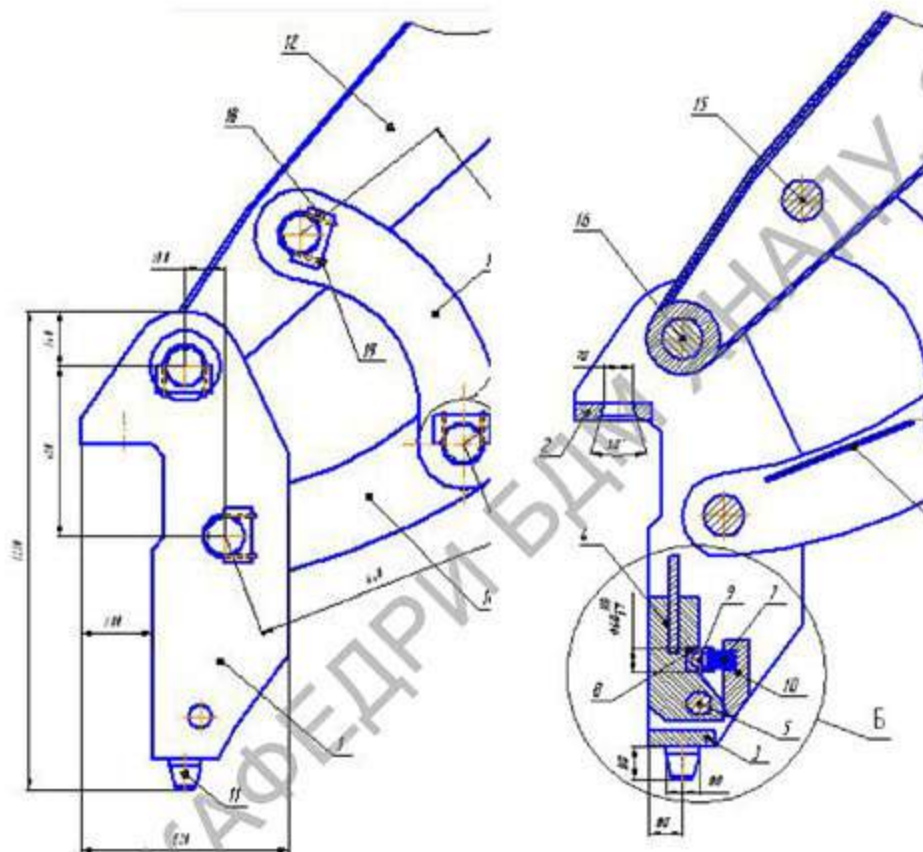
Адаптер пристрою для швидкої заміни робочого обладнання
